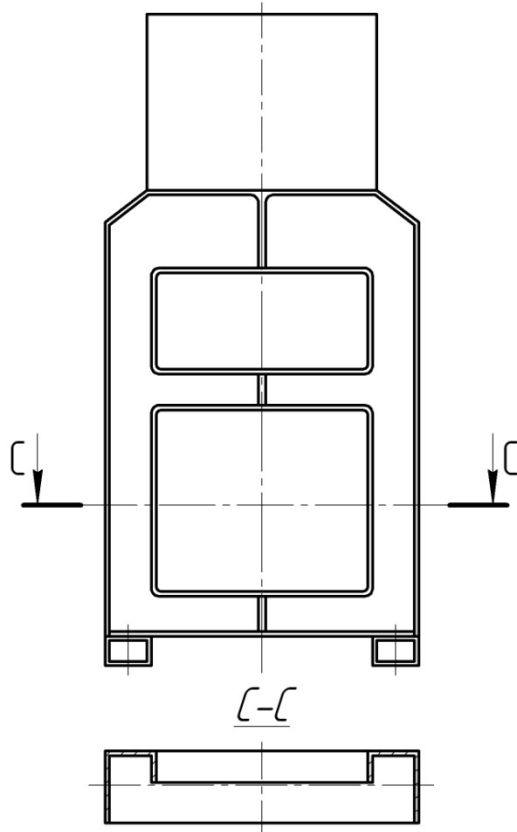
Конструкция станины вырубочного прессы (вид E на рис. 1)
